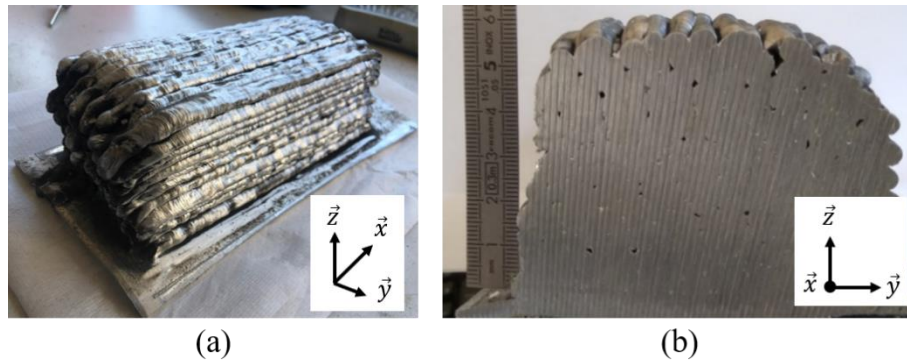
Vue de profil et d'une coupe transversale d'un bloc fabriqué en utilisant le mode de transfert CMT-P et l'inclinaison de la torche de soudage à 45°.
